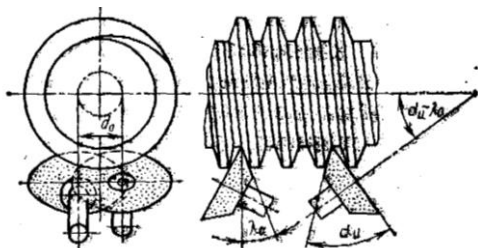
Схема шліфування евольвентного черв'яка чашковим кругом
